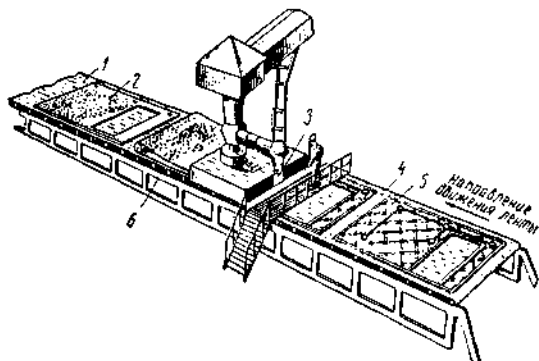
Изготовление на прокатном стане гипсобетонной перегородки с электропроводкой
